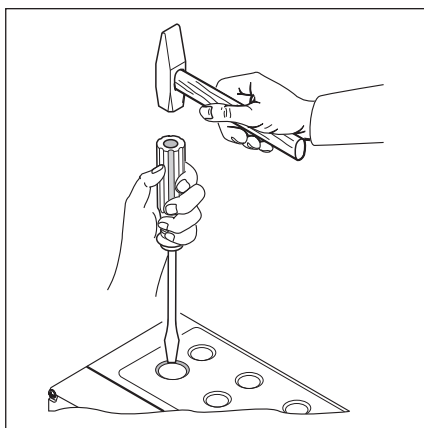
Для дооснащения кабельной арматурой с резьбовым соединением выбивайте предварительно выдавленные места гнезд только при закрытой крышке.
